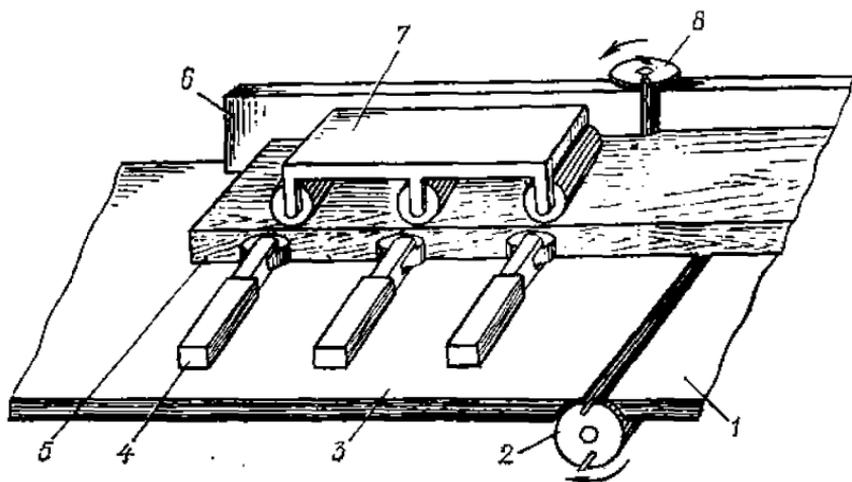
Схема станка для двустороннего фугования заготовок с механической подачей
